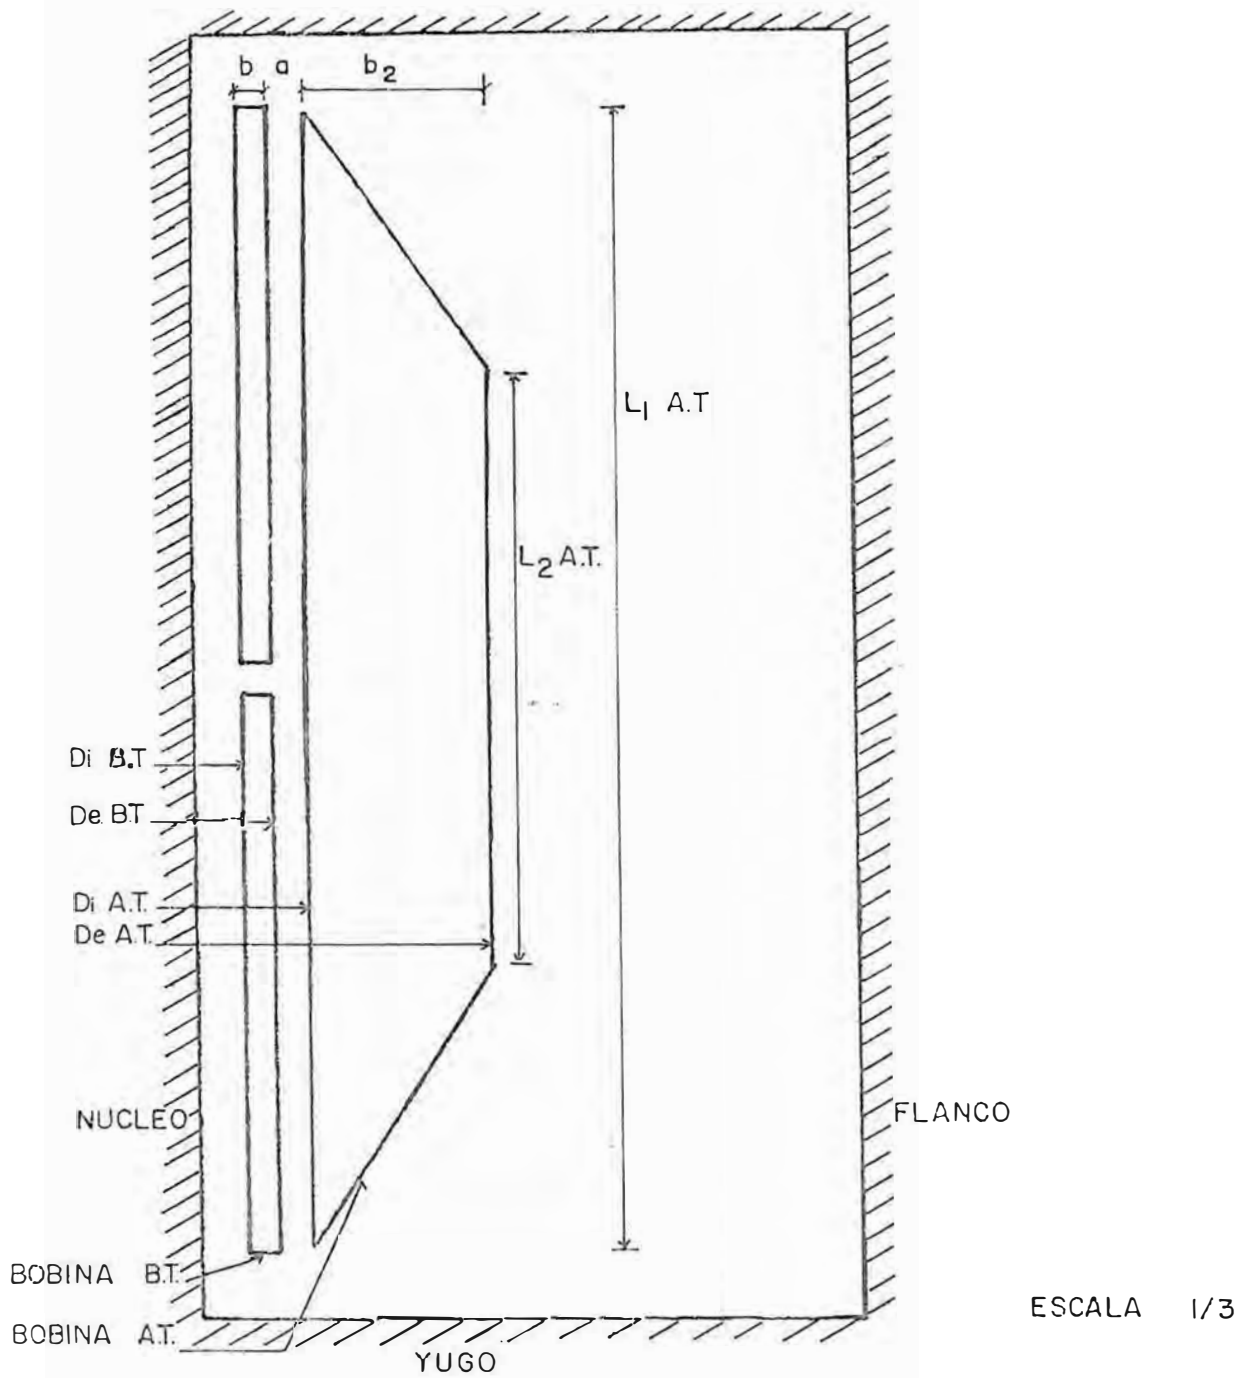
DIMENSIONES DE LA BOBINA
